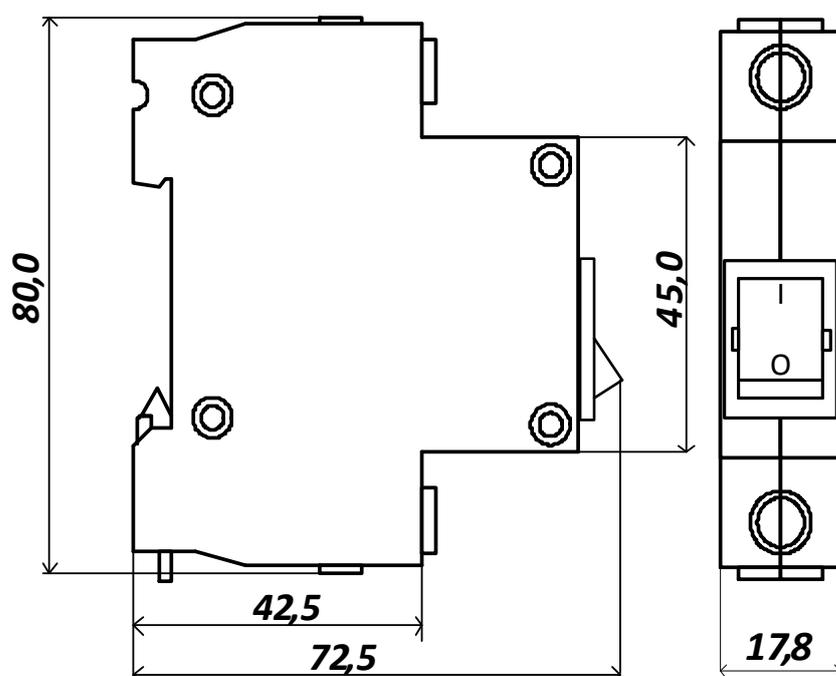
Габаритные размеры устройства Commeng OCP
